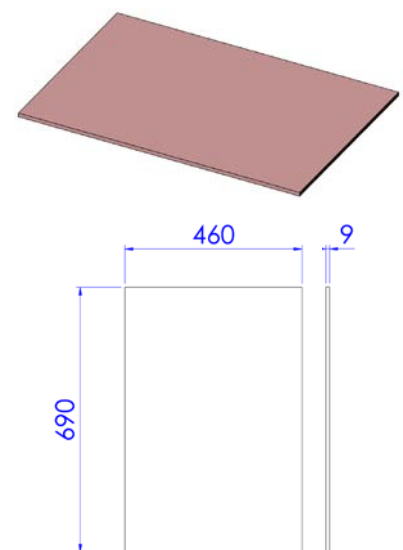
Reinigungsmatten Dimensionen (mm)
